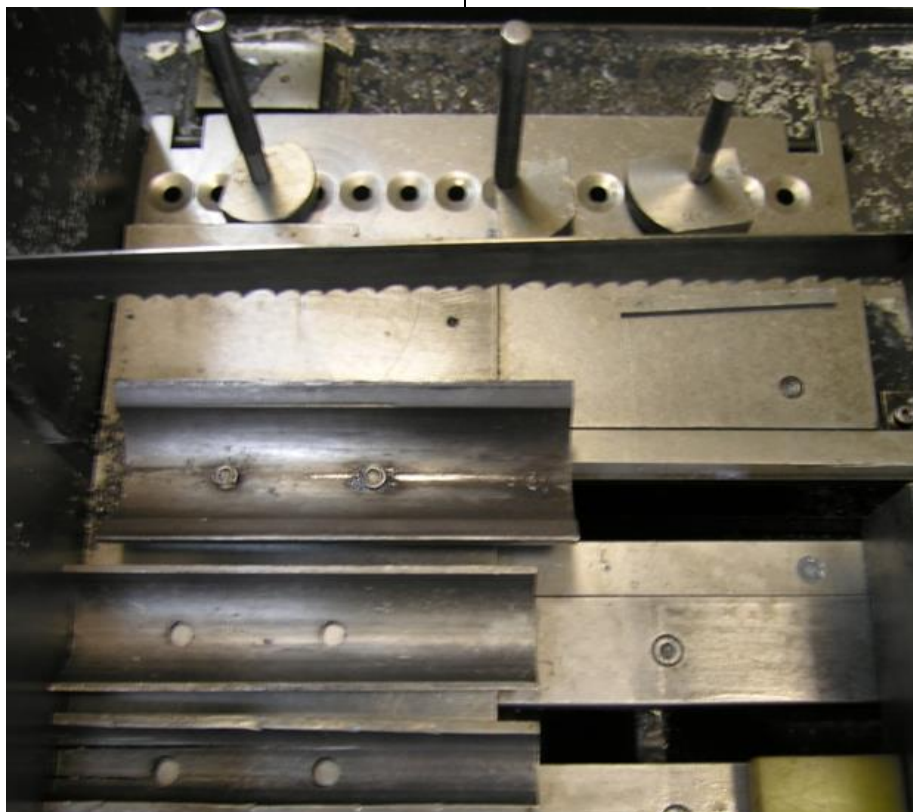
Общий вид составных частей приспособления для крепления патрубков в ленточнопильном станке
